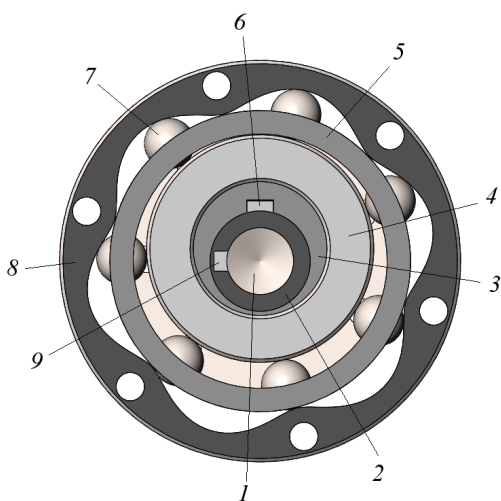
Схема зацепления планетарной шариковой передачи
